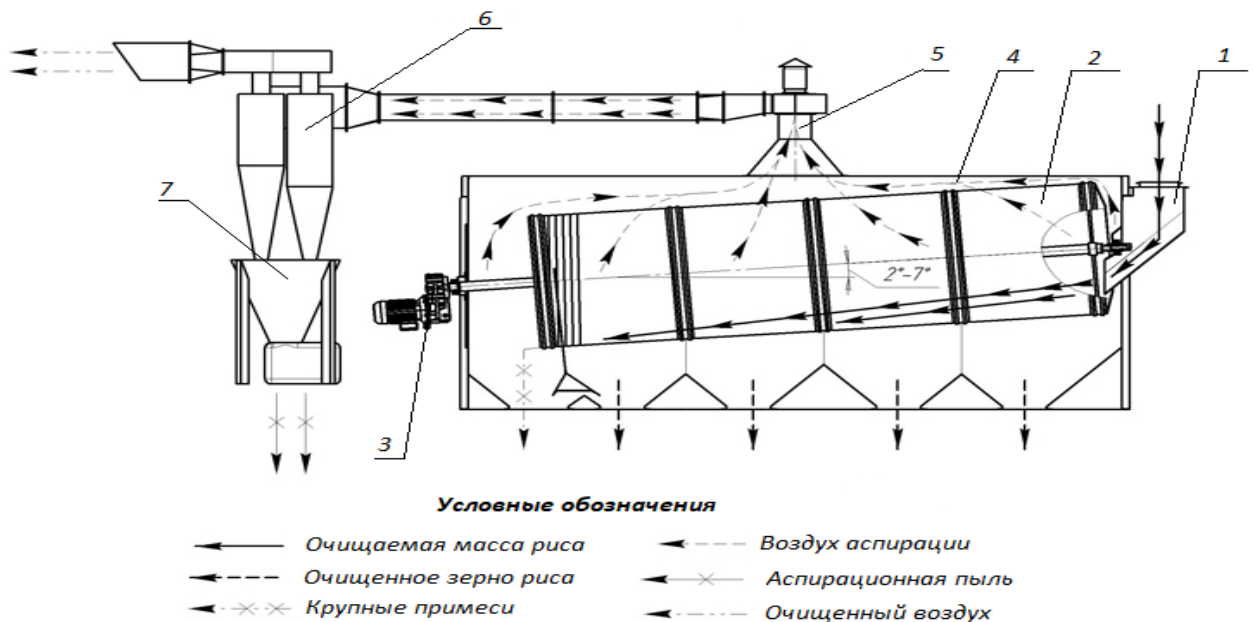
Конструктивно-технологическая схема установки для первичной очистки рисовой массы: 1 – патрубок; 2 – барабан; 3 – привод барабана; 4 – корпус
